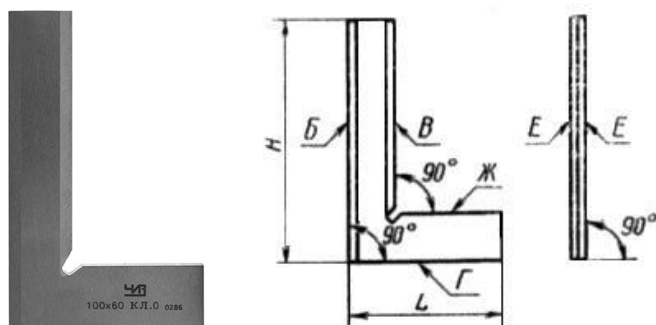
Общий вид угольников УЛП, обозначение основных размеров и поверхностей
